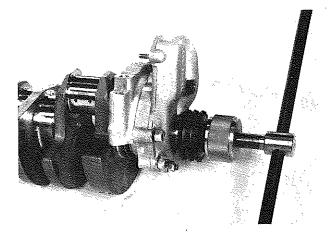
Smontare II pignone distribuzione e la pompa olio Disassemble distributor pinion and oil pump
